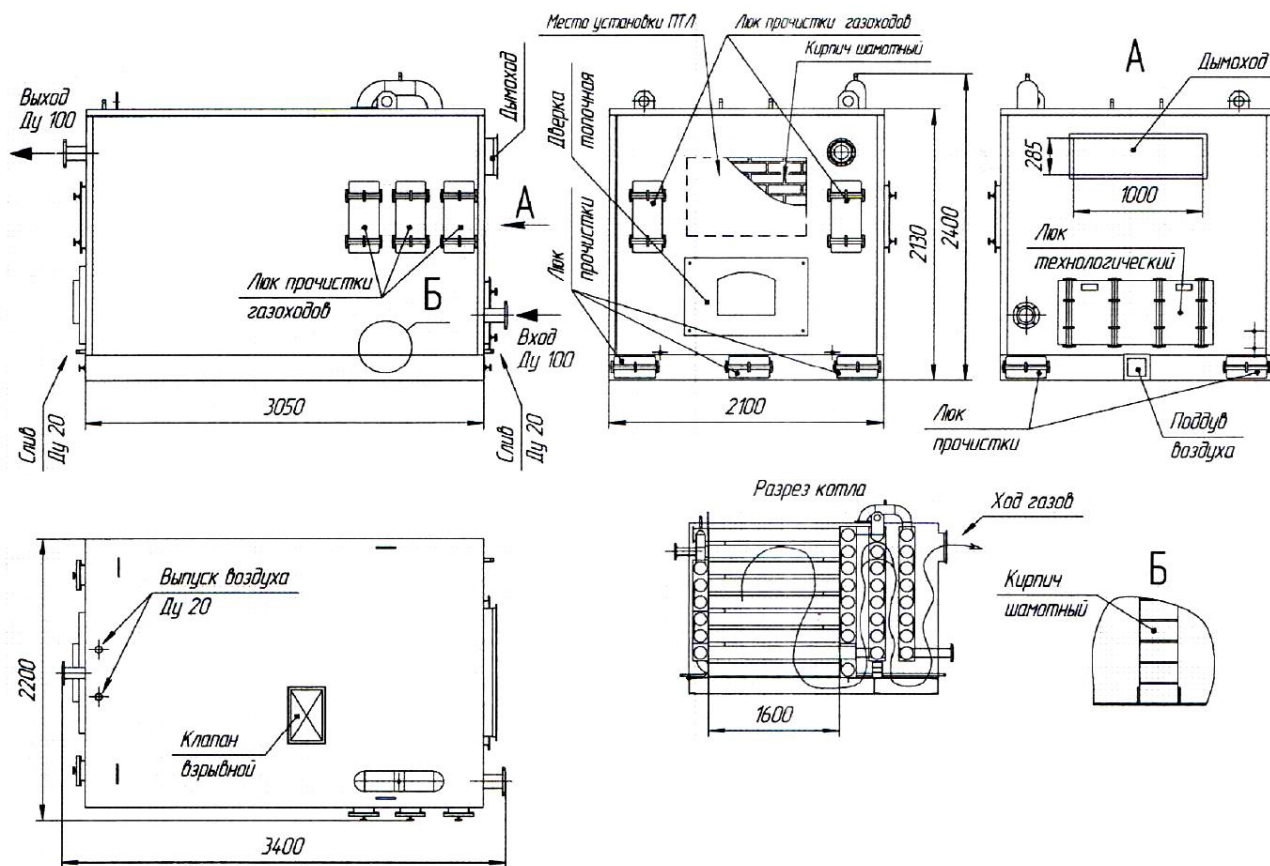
Устройство и габариты компоновки котла КВр-1,16 ОУР
